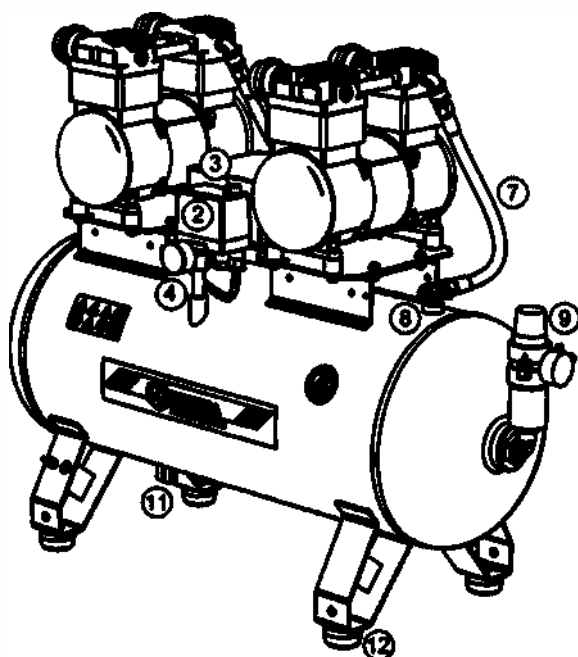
Общий вид компрессора KM-100.OLD15T и KM-100.OLD20T
